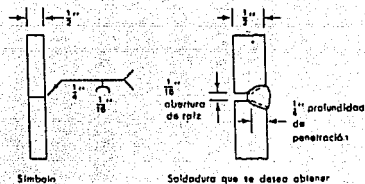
Símbolo de soldadura de acanaladura en "U" y soldadura que se desea obtener.
